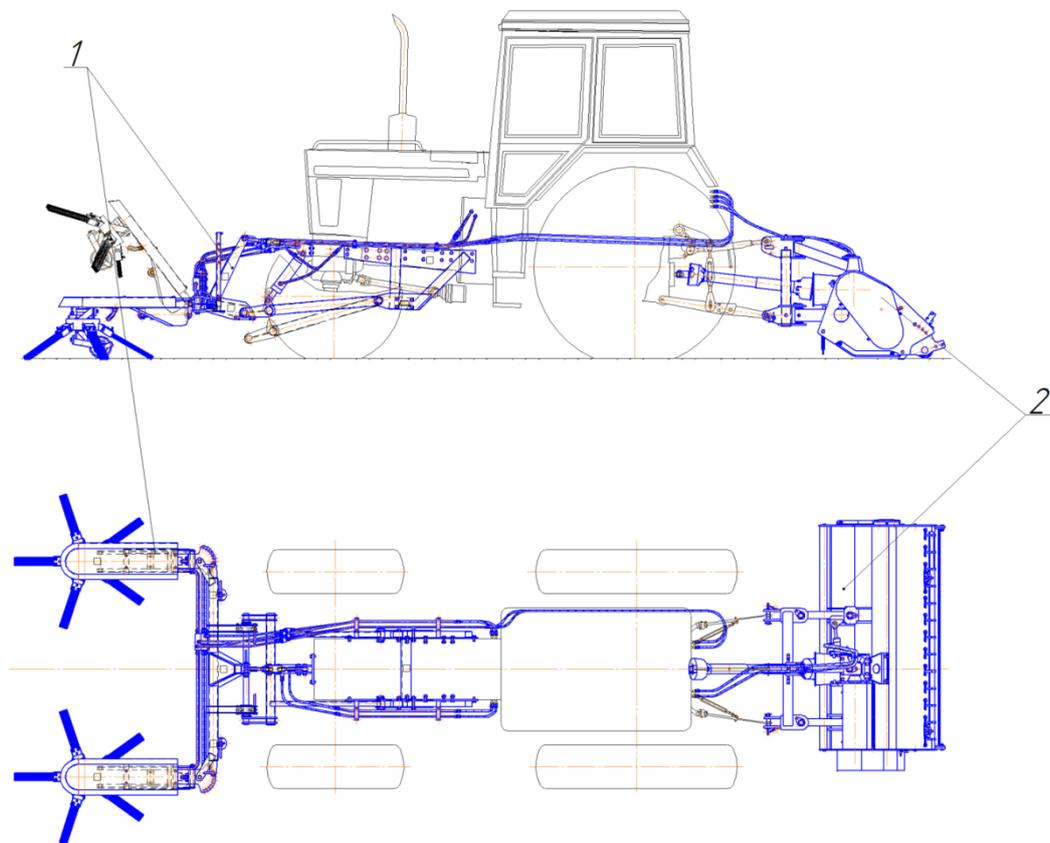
Схема размещения валкователя и измельчителя на тракторе
